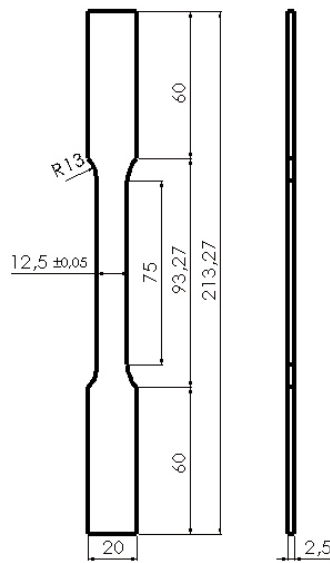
DIMENSIONAL DO CORPO DE PROVA
